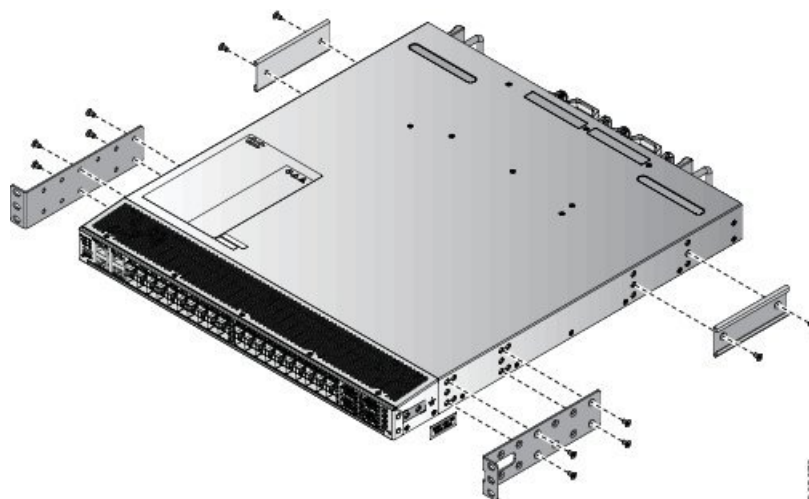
Suportes de montagem em rack na parte frontal do Cisco NCS 5001
